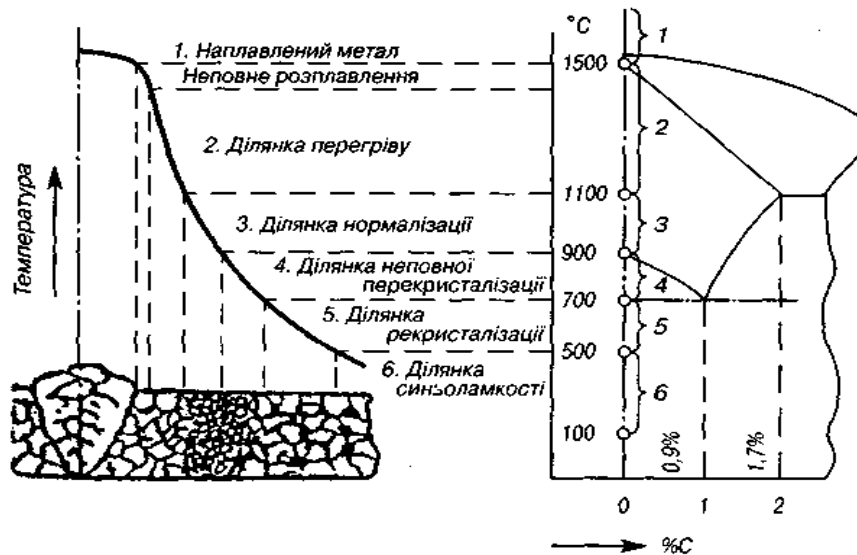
Схема структур, що утворюються при зварюванні стикового з'єднання з маловуглецевої сталі за один прохід
